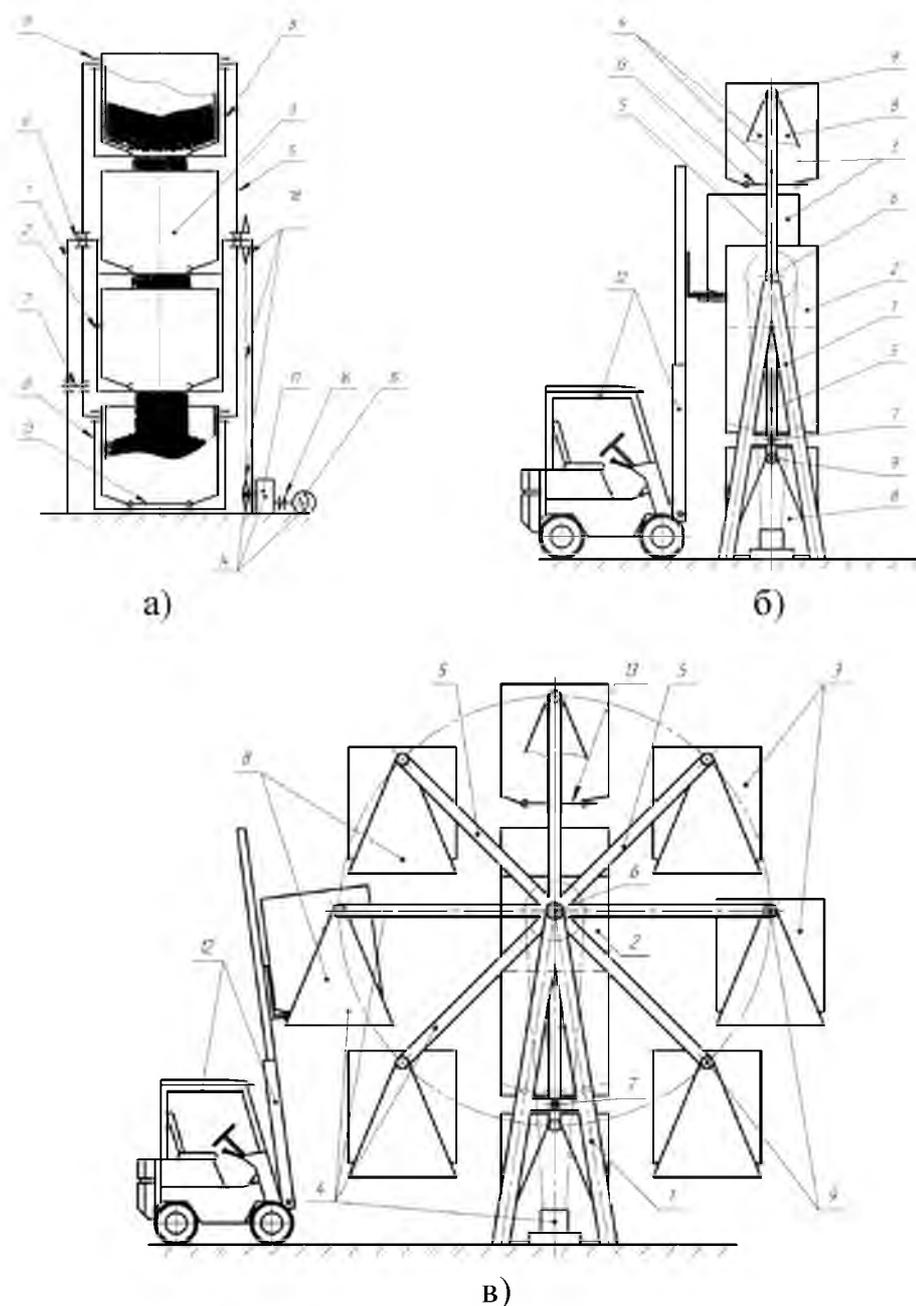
Устройство для приготовления смесей семян сортов пшеницы:
